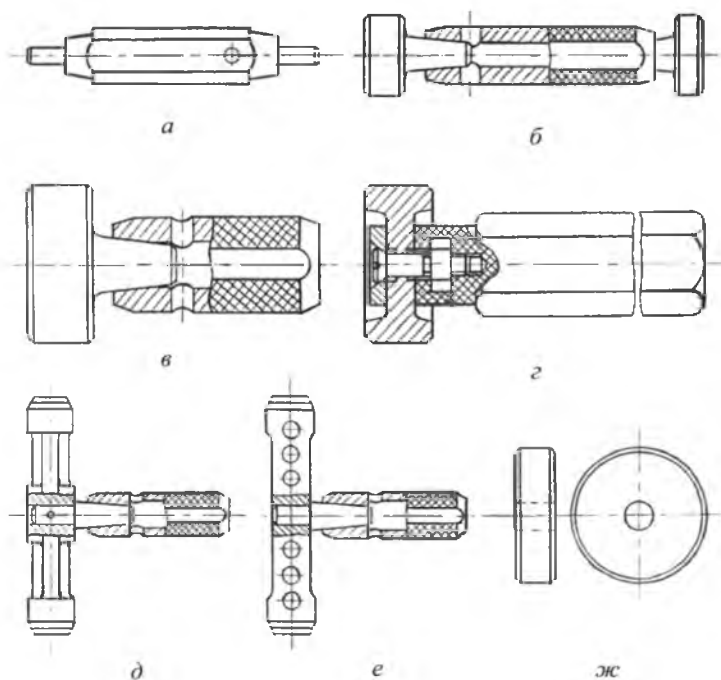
Основные типы калибр-пробок для контроля отверстий и контрольный калибр к скобам: *а* – пробка двухсторонняя со вставками ( $D = 1...6$  мм); *б* – пробка двухсторонняя со вставками ( $D = 3...50$  мм); *в* – пробка проходная (непроходная) со вставками ( $D = 52...75$  мм); *г* – пробка штампованная проходная (непроходная) с насадками ( $D = 52...100$  мм); *д* – пробка проходная (непроходная) неполная ( $D = 102(75)...160$  мм); *е* – пробка проходная (непроходная) неполная ( $D = 102(75)...300$  мм); *ж* – шайба полная ( $D = 18...100$  мм)
